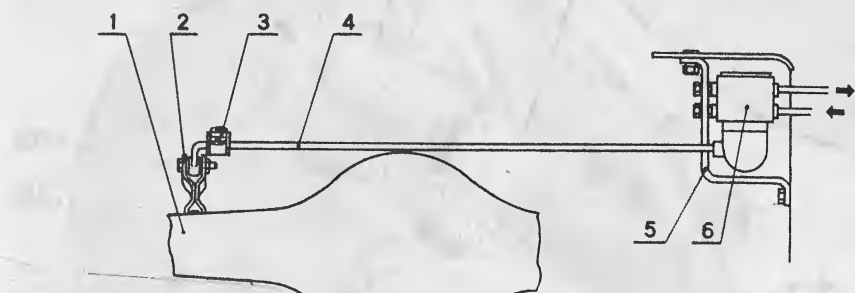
Установка регулятора: 1 — балка заднего моста; 2 — серьга; 3 — скоба; 4 — торсион; 5 — кронштейн кузова; 6 — регулятор.
